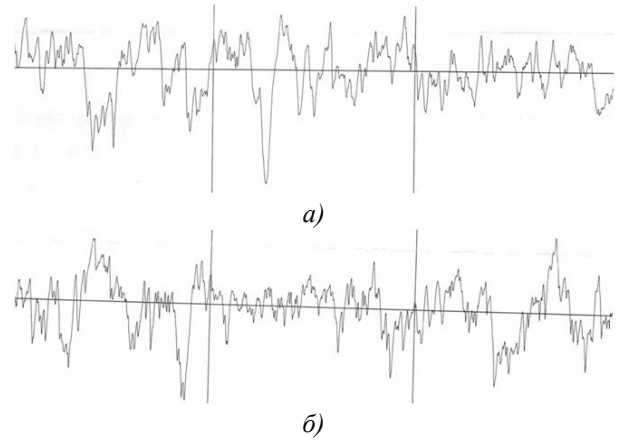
Шероховатость поверхности образца 1, измеренная на 3-х базовых длинах  $l = 0,8$  мм: а – исходная шероховатость; б – шероховатость после поверхностного упрочнения
